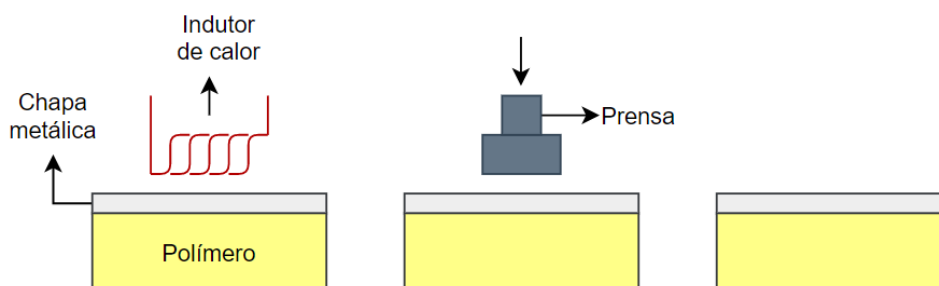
Princípio da soldadura por indução. Adaptado de [36].
